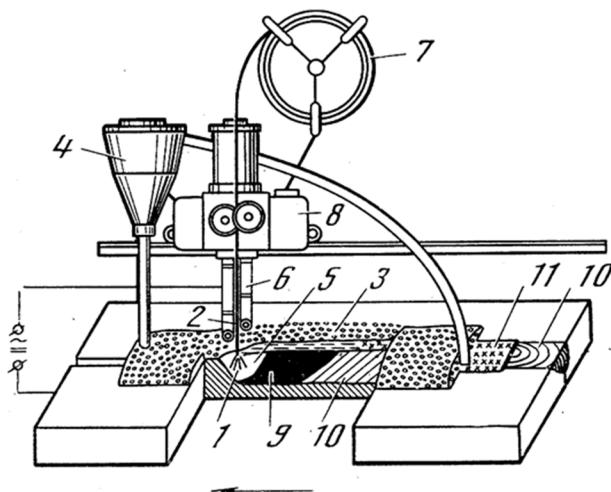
Схема автоматической дуговой сварки под слоем флюса:
